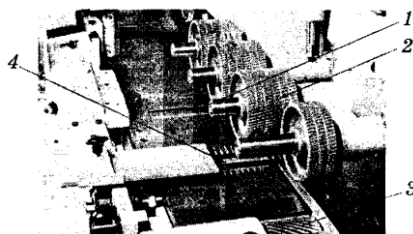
Вальцевий подавальний механізм чотирибічного верстата: 1 — нижній гладкий подавальний валець; 2 — верхній рифлений подавальний валець; 3 — нижній рифлений подавальний валець; 4 — ножова головка
